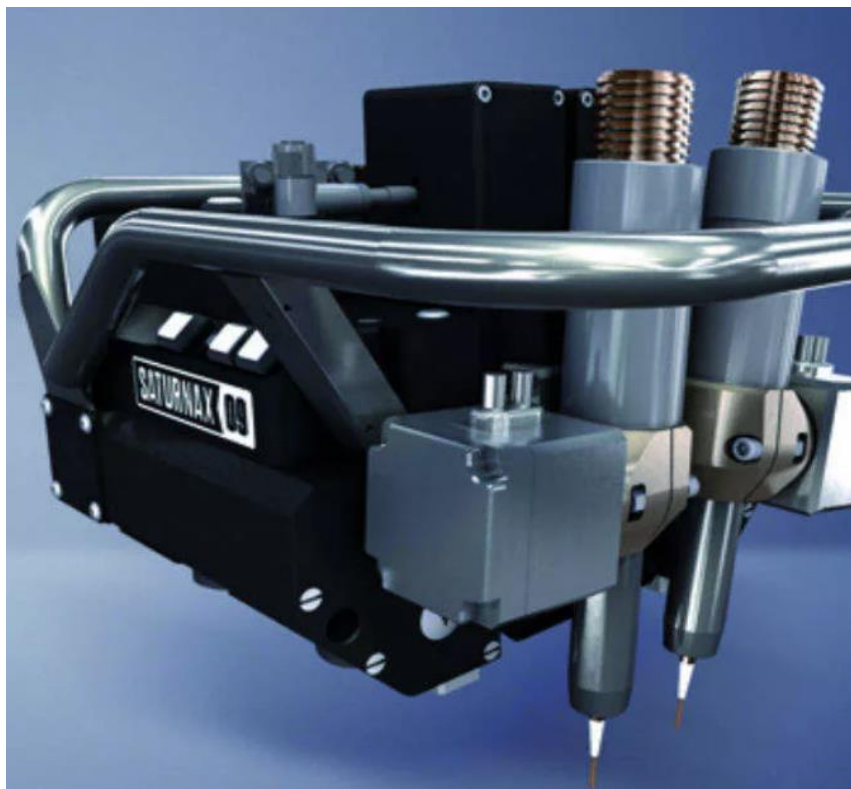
Сварочная головка комплекса «Saturnax»
